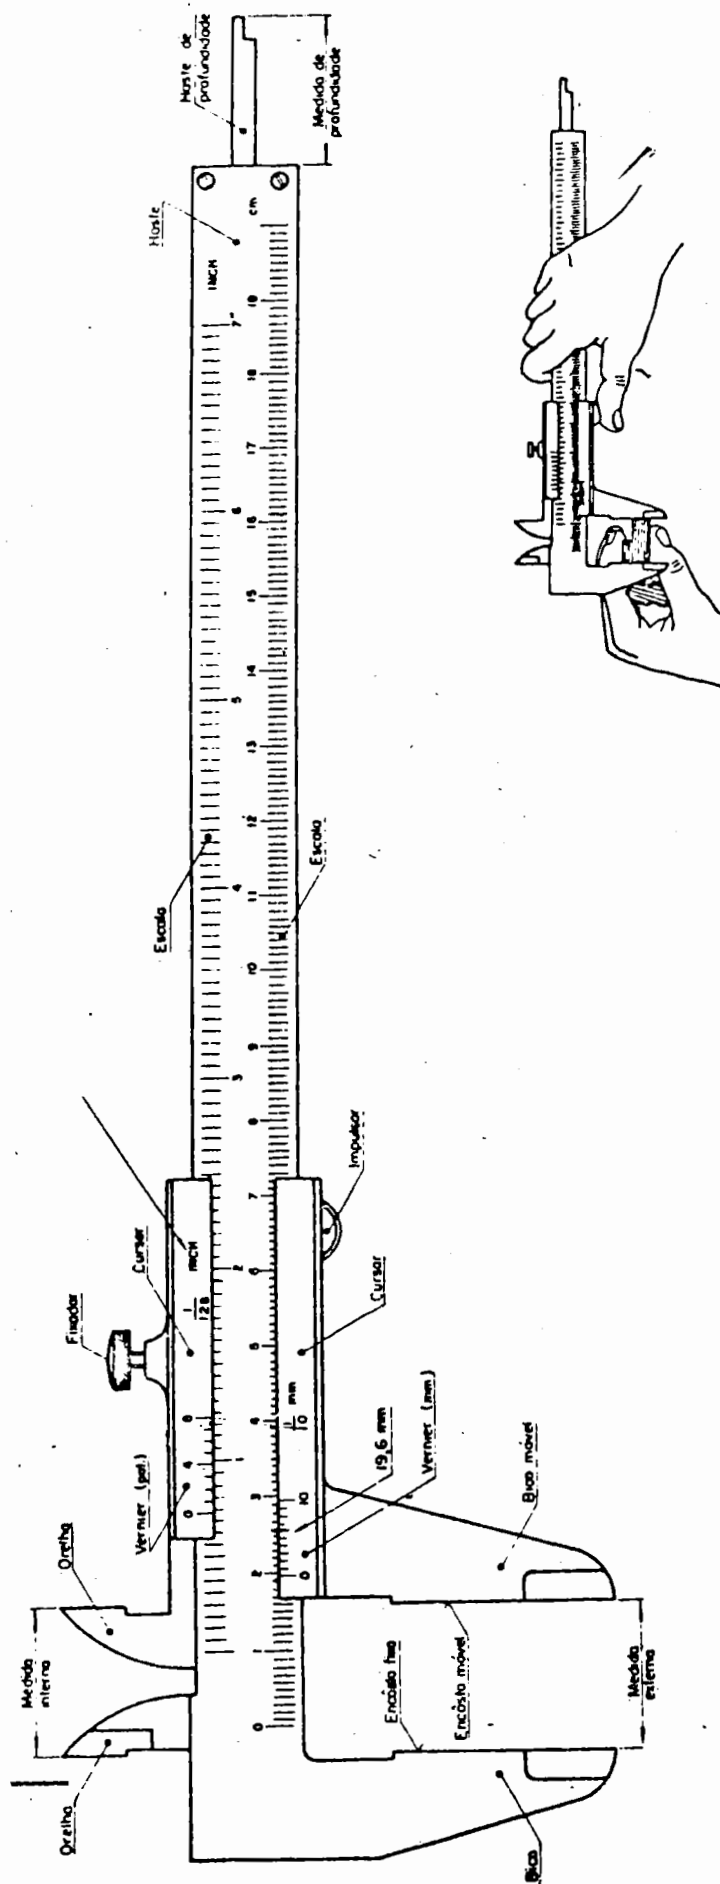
Paquímetro com vernier de 1/10 mm
